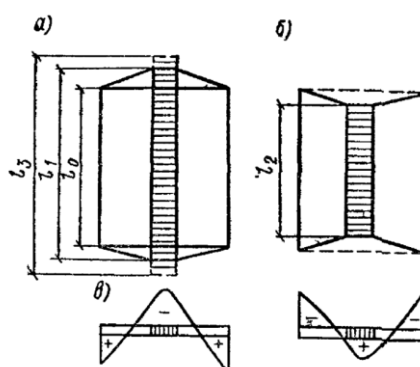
Характер деформации стального листа при сварке стыкового шва: а — удлинение l_1 , вызванное нагревом при сварке; б — укорочение l_2 после остывания; в — эпюры напряжений при сварке и после охлаждения; l_0 первоначальный размер листа; l_3 — размер после нагрева.
